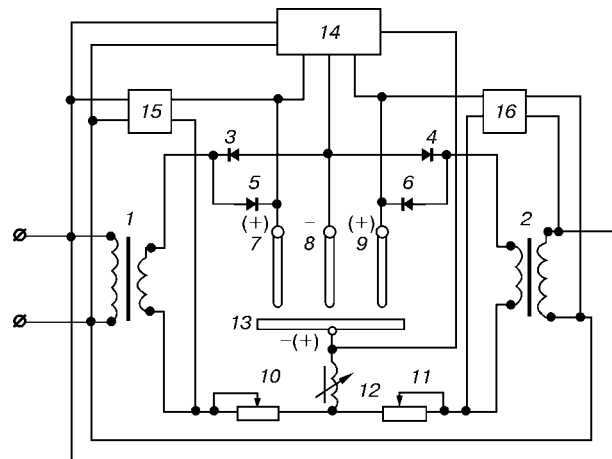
Принципиальная схема устройства для плазменной и дуговой сварки (обозначения поз. 1–16 приведены в тексте)
